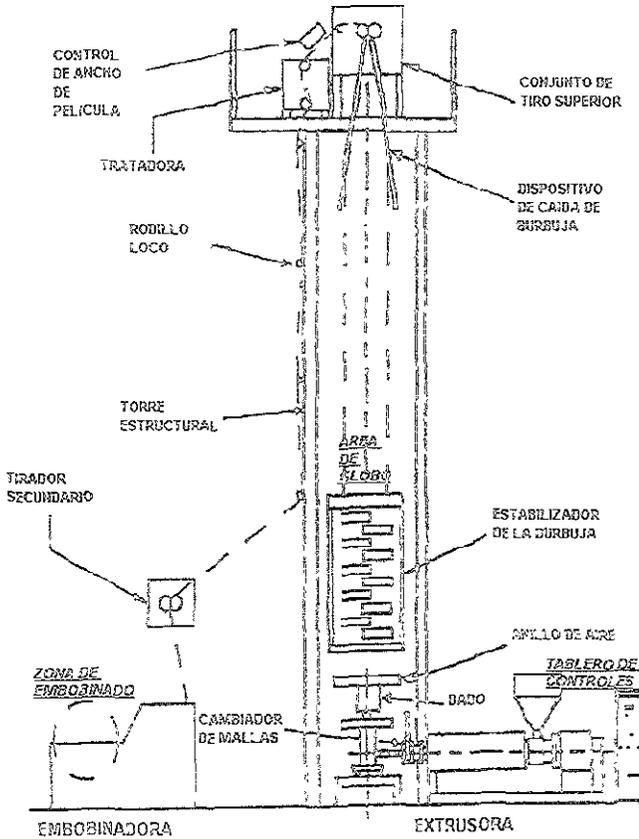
Partes de una máquina extrusora de bolsas.
